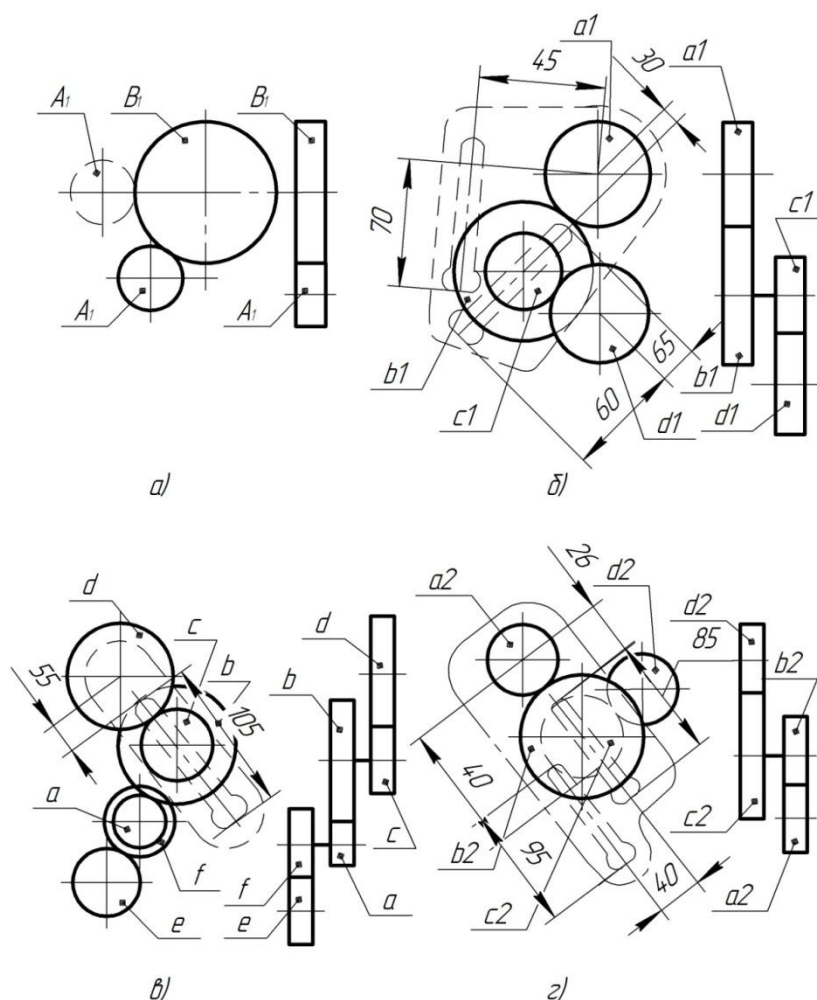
Гитары зубчатых колес зубофрезерного станка мод. 5Д32: а — гитара скоростей; б — гитара подачи; в — гитара деления; г — гитара дифференциала
